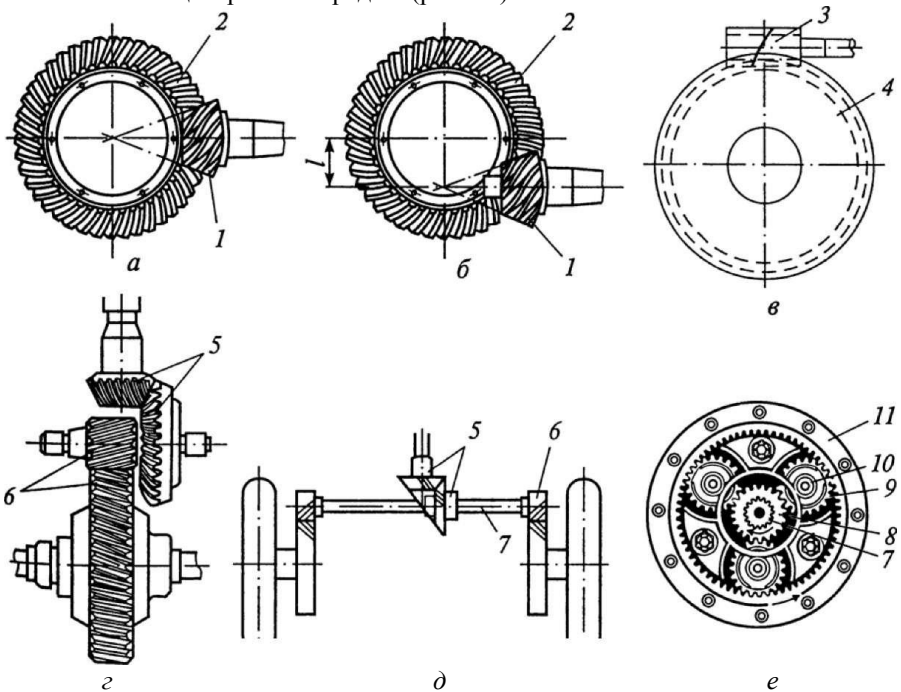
Типи головних передач: а - конічна; б - гепіідна; в - черв'ячна, г - подвійна центральна; д - подвійна рознесена; е - планетарна; 1 - привідна шестерня; 2 – ведена шестерня; 3 - черв'як; 4 - черв'ячне колесо; 5 перший ступінь передач; 6 - другий ступінь передач; 7 - піввісь; 8 - сонячна шестерня; 9 - сателіт; 10 - вісь; 11 - коронна шестерня.
